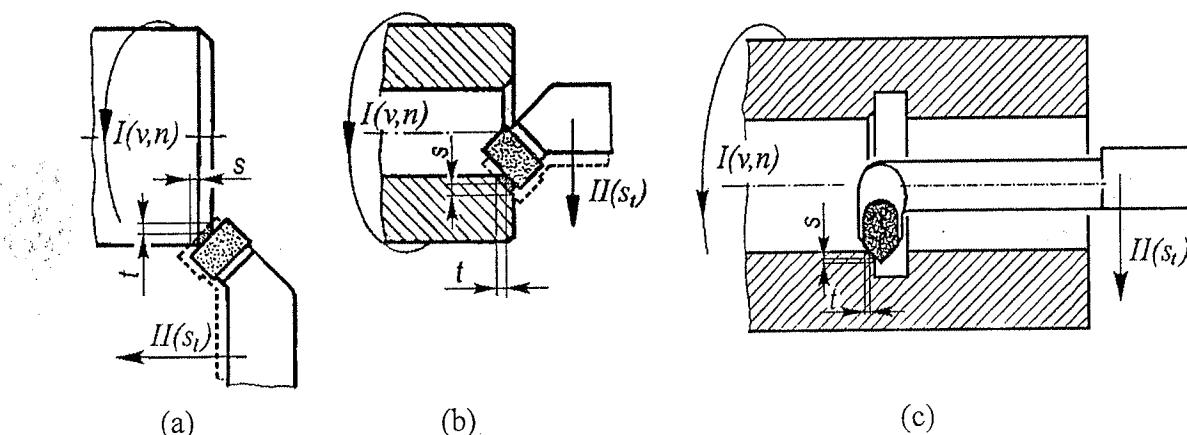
Strunjirea canalelor: (a) canal transversal cilindric exterior; (b) canal transversal cilindric interior; (c) canal frontal
